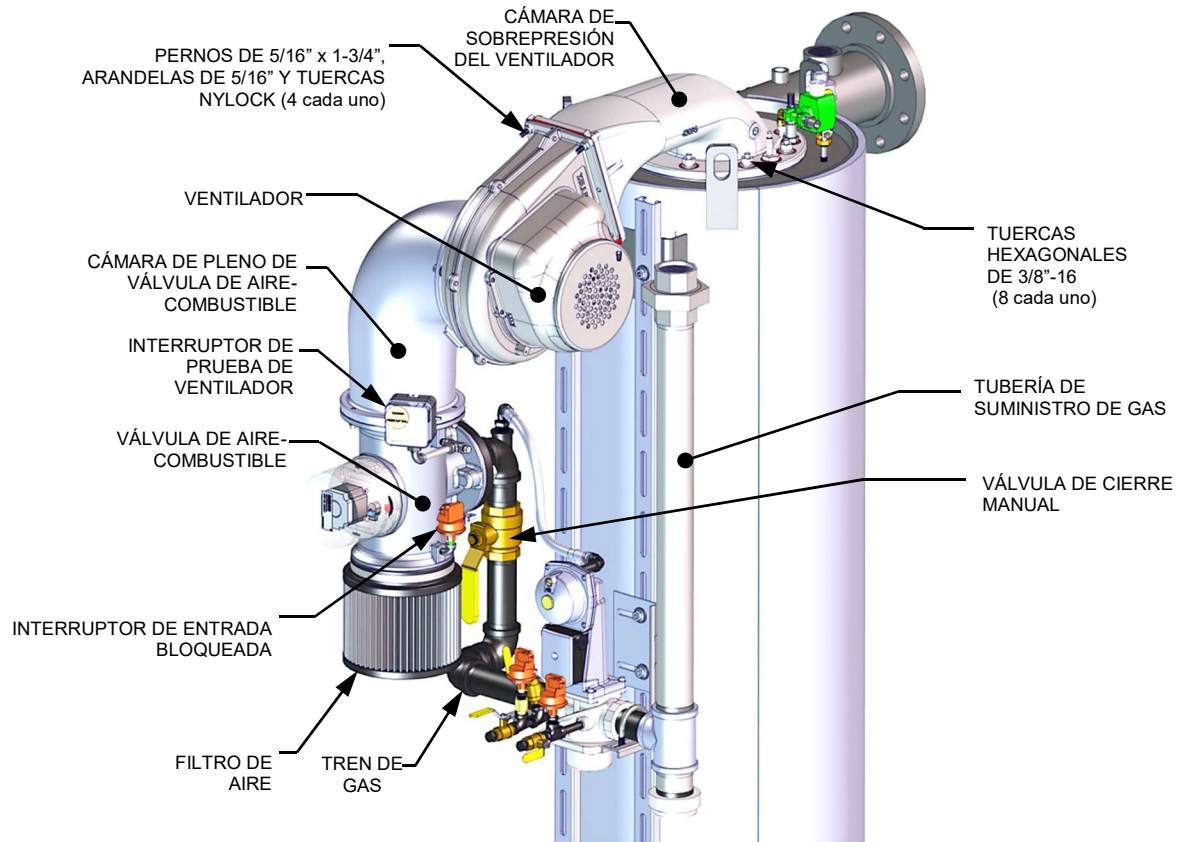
Información de montaje de ensamblado del quemador de BMK 1500/2000
